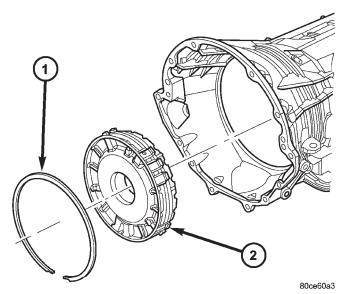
Desmontaje de retén y tapón de embrague de 4ª
